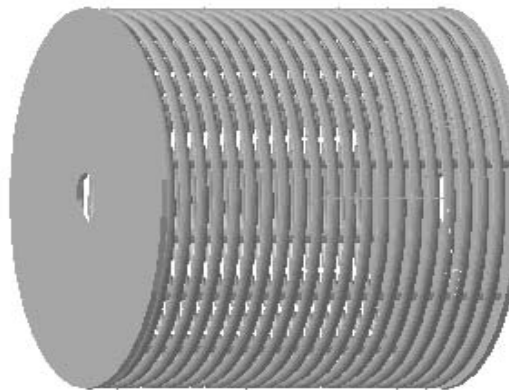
Циліндричний барабан із прутковою поверхнею
